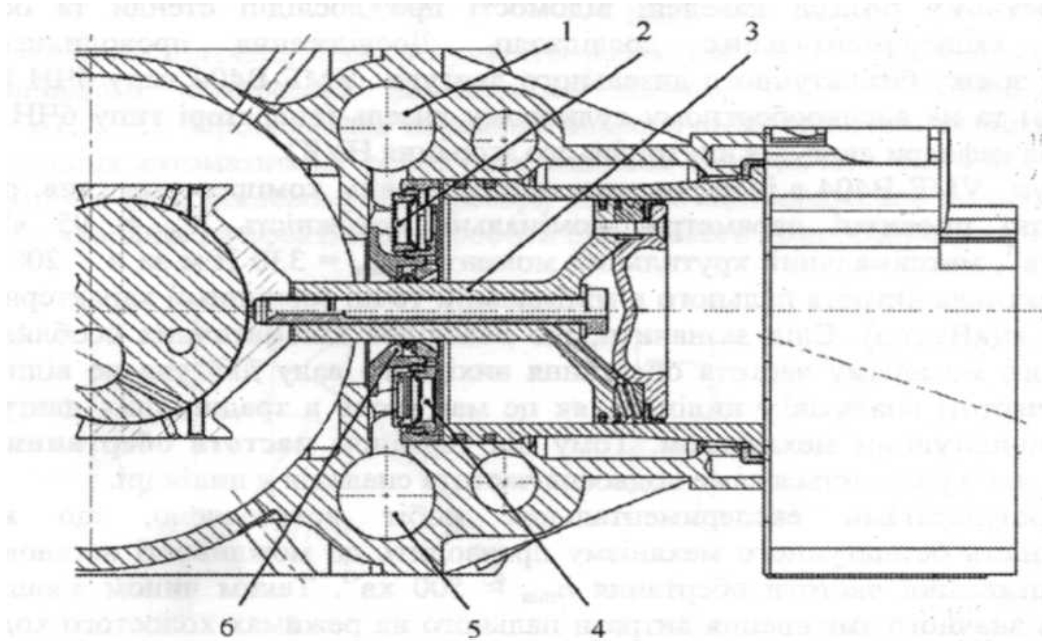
Робочий циліндр двигуна з підпоршневим компресором:
